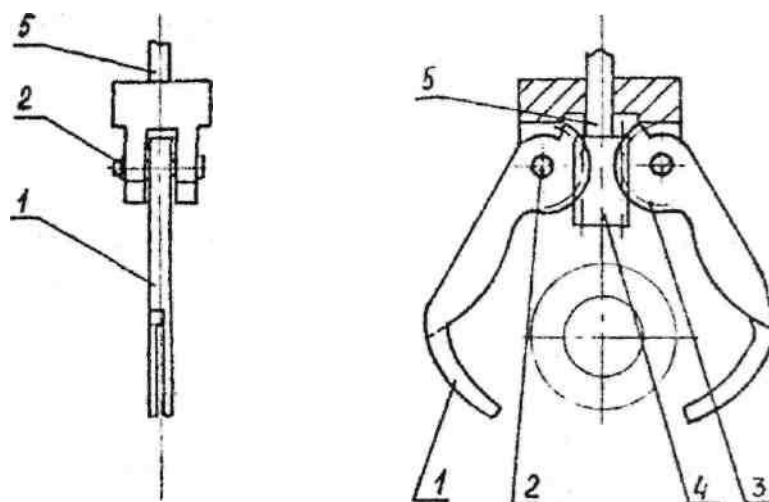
ЗУ для фланцев с губками специального профиля и реечным передаточным механизмом
